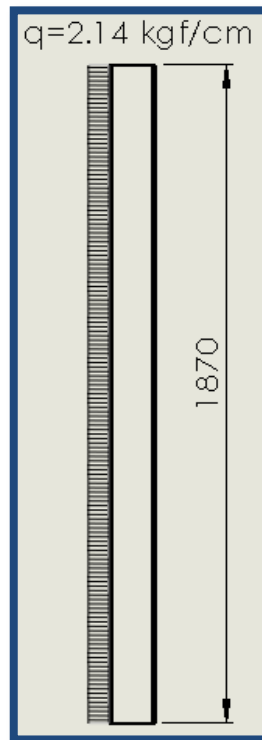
Estado de carga del parante utilizado para el cálculo de la soldadura.
